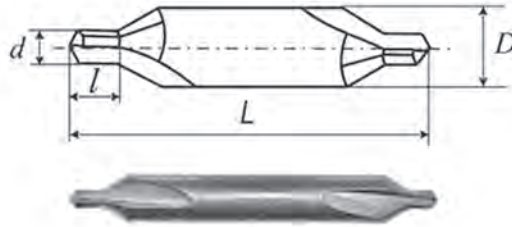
Зовнішній вигляд і параметри центровочного свердла
